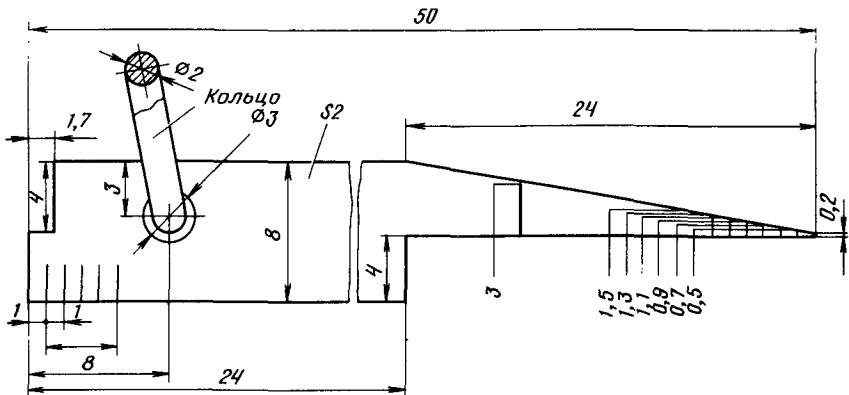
Шаблон для измерения зазора между лабиринтным кольцом и корпусом букасы и проверки смещения корпуса буксы относительно лабиринтного кольца
